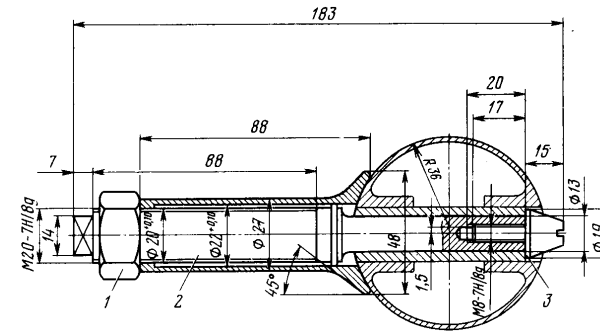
Приспособление для выпрессовки поршневого пальца: 1 — гайка; 2 — оправка; 3 — наконечник
